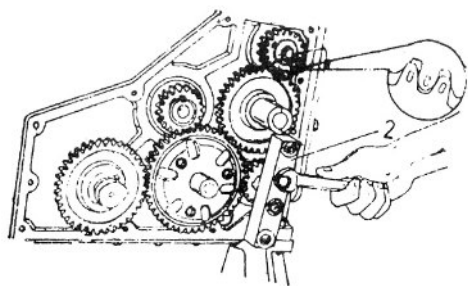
As engrenagens sendo desmontadas por meio de um sacador, com as marcas de balanceamento nos dentes.
